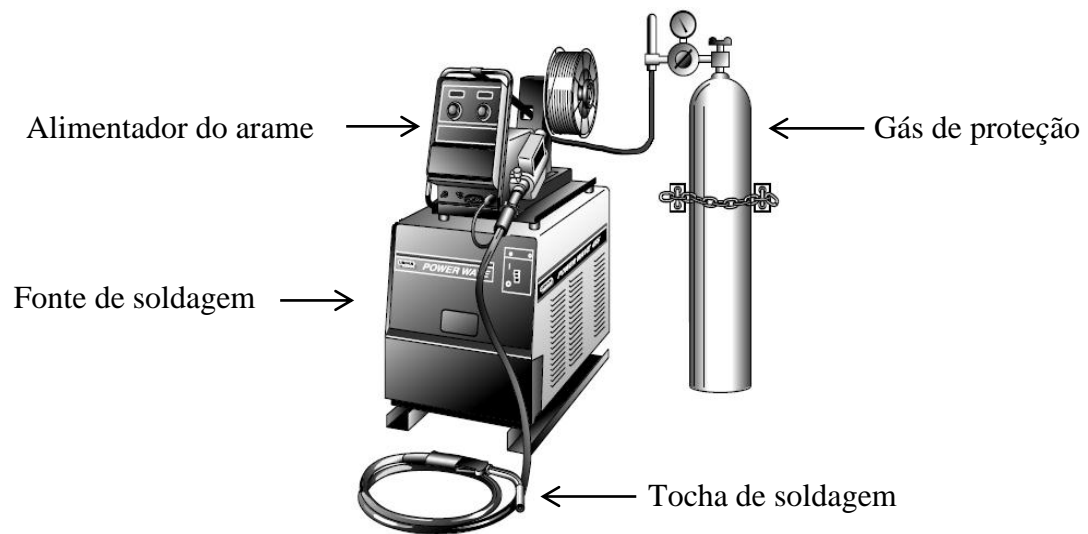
1: Equipamentos básicos de soldagem GMAW (Modificado Nadzam, 2011).
